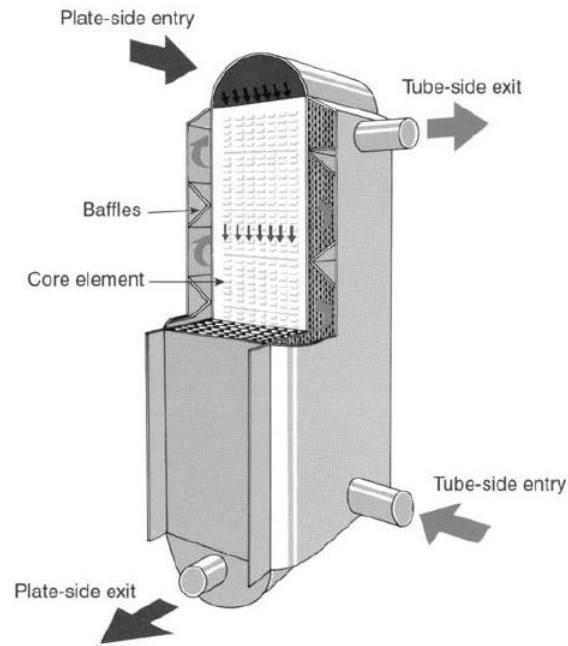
Intercambiador de Placas Soldado. [1]
